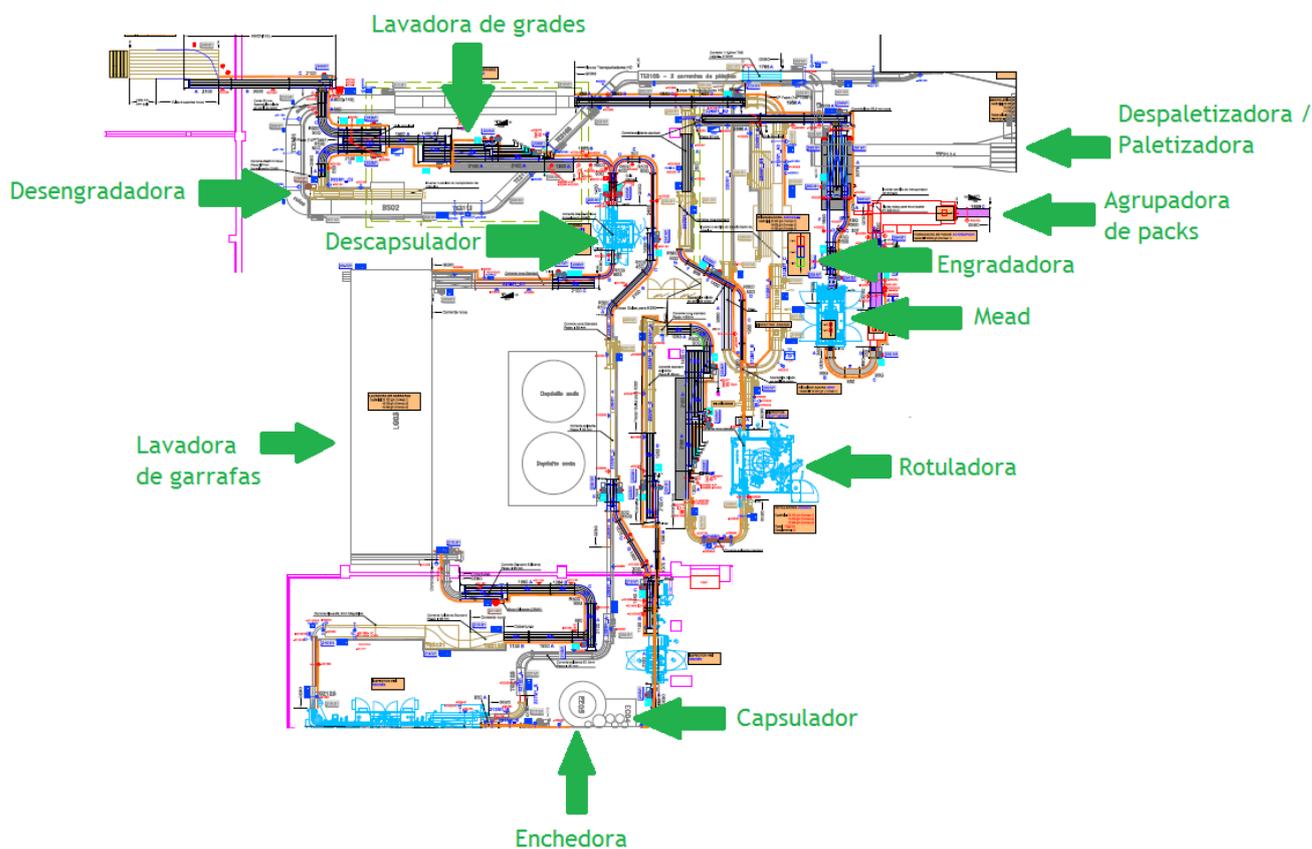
Layout linha 1 (Fonte: Adaptado de SAL, 2015)
